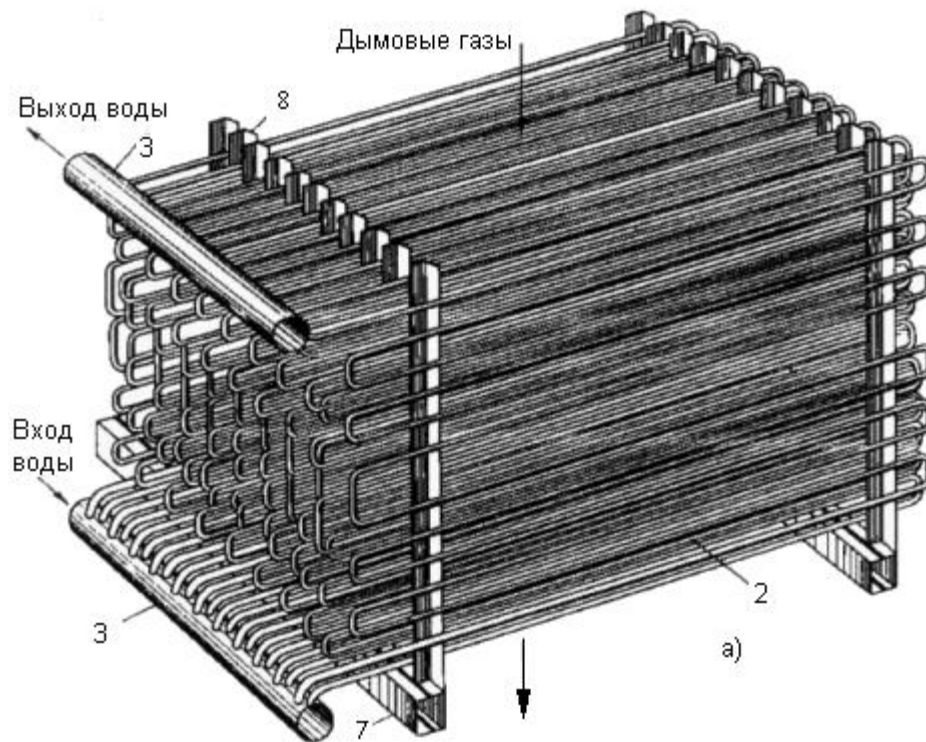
а Общий вид пакета экономайзера: 2 - трубные змеевики; 3 - коллектор; 7 - опорная балка; 8 - опорные стойки.
